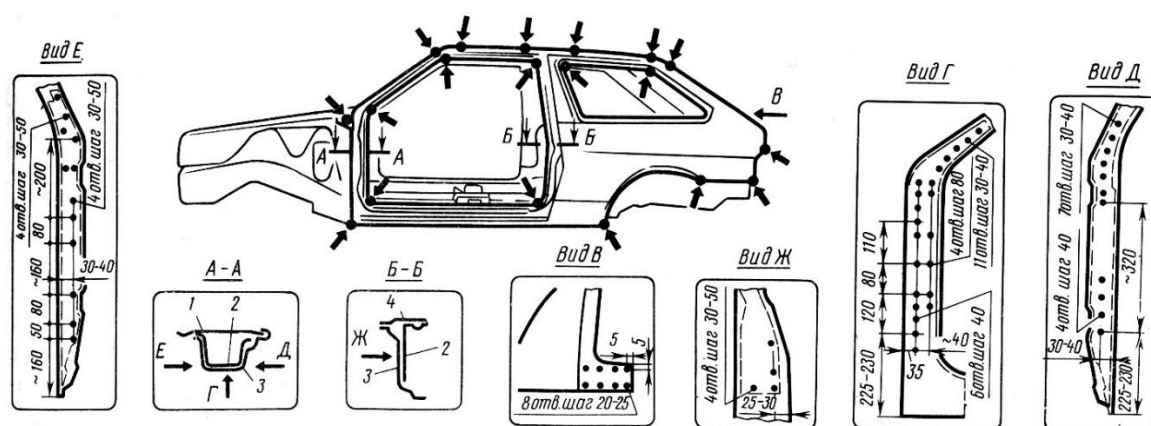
Точки зварювання боковини вздовж стійки кузова
